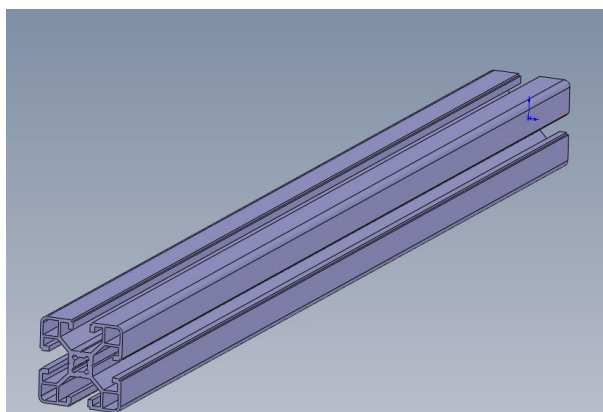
Алюминиевый конструкционный профиль серии 40*40
